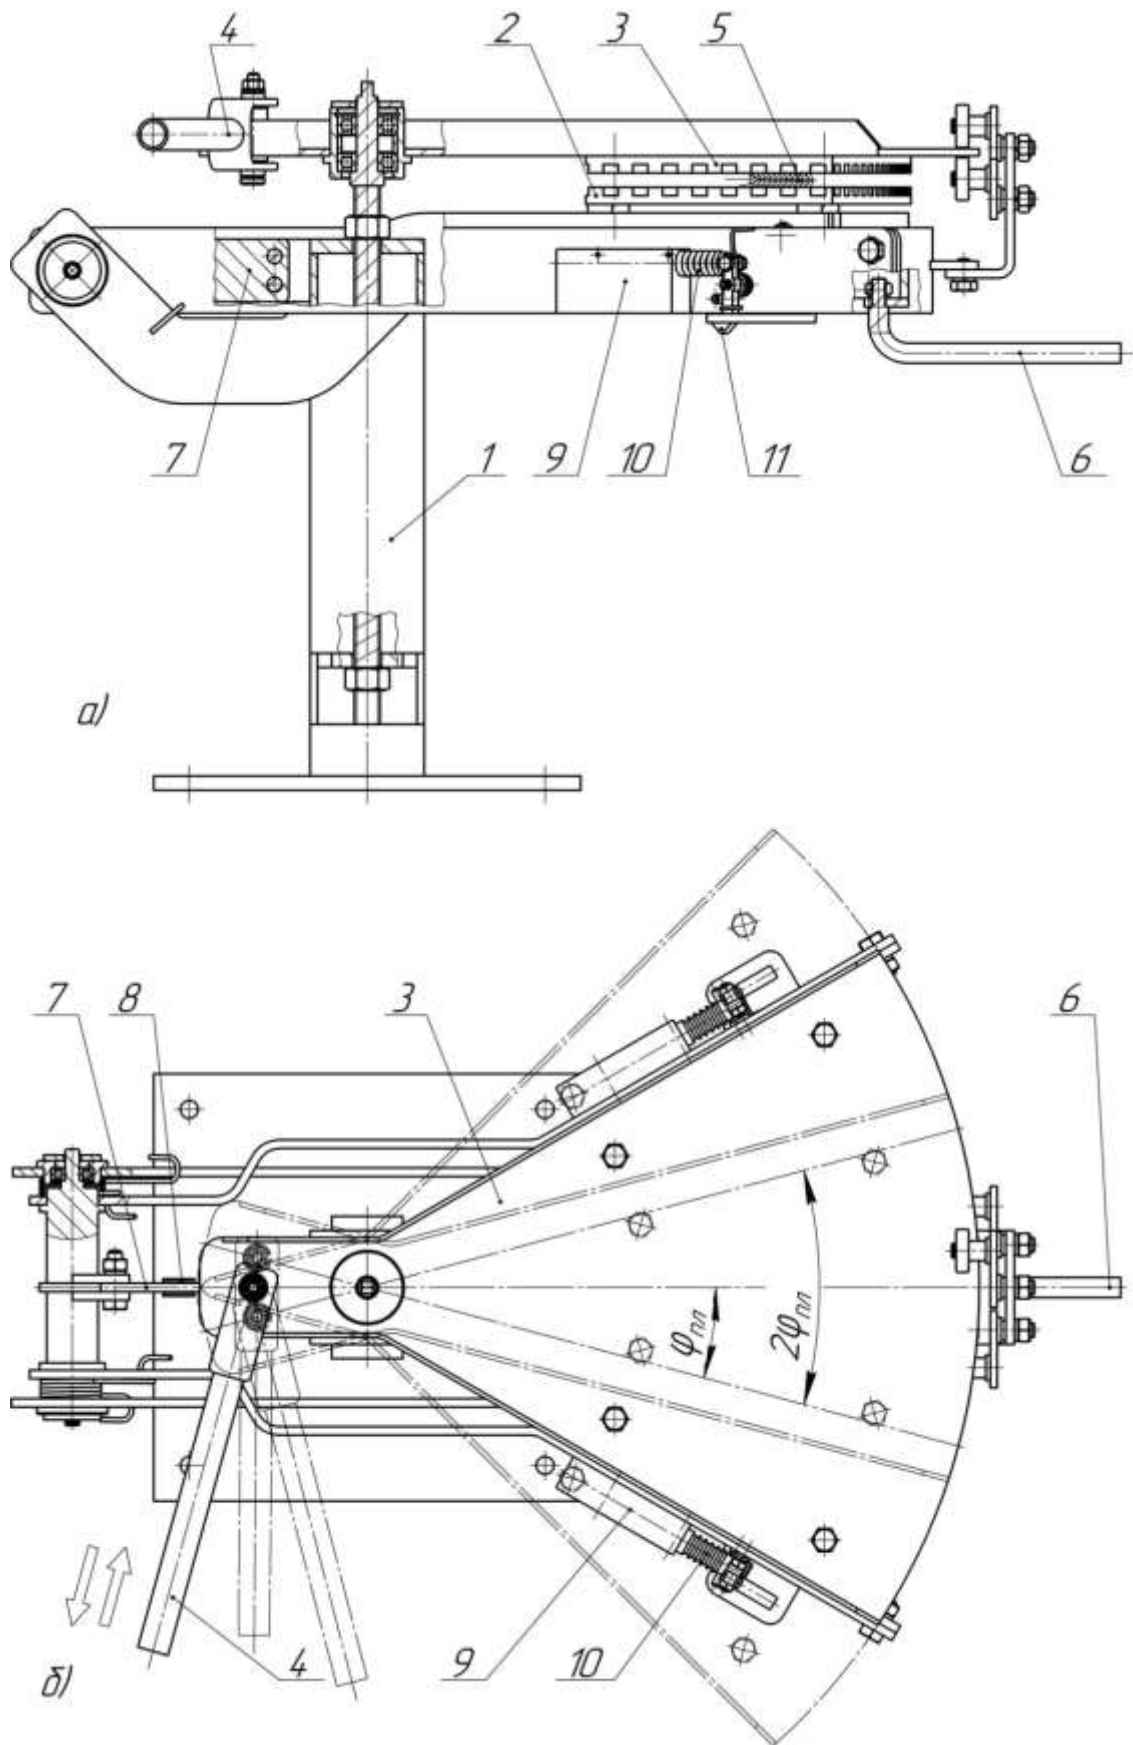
Схема экспериментальной молотильной установки (Патент РФ № 2483525): *a)* главный вид; *б)* вид сверху; 1 – стойка; 2 – дека; 3 – верхняя площадка; 4 – привод; 5 – колос; 6 – ручка; 7 – тензопластина; 8 – тензодатчики; 9 – электромагнит; 10 – шток; 11 – защелка
